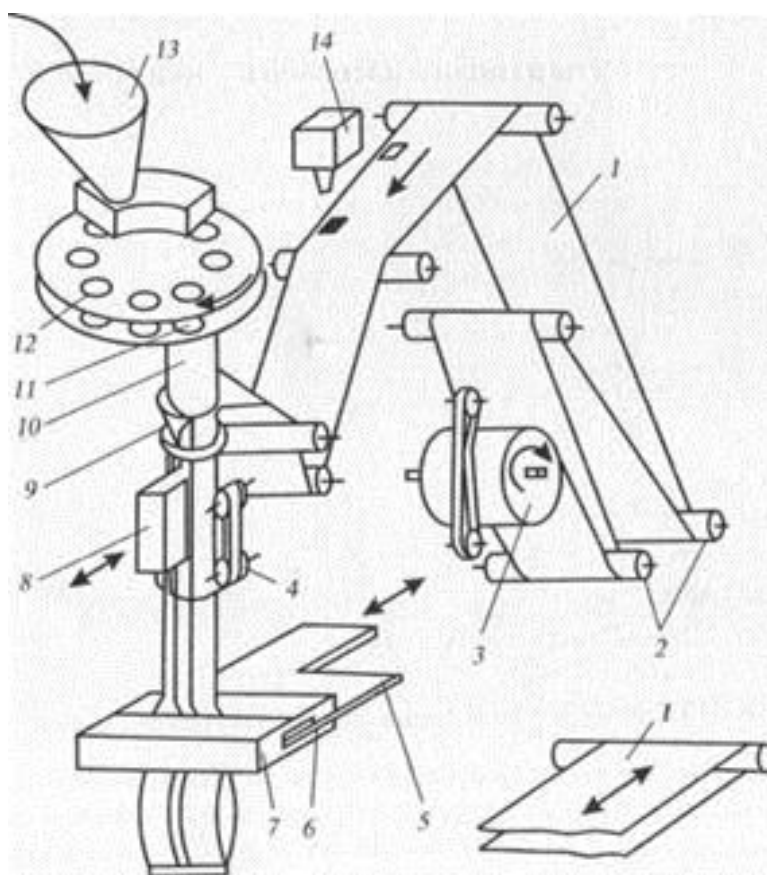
Технологічна схема автомата А5-КЛШ: 1 – полімерна стрічка; 2 – направляючі ролики; 3 – рулон стрічки; 4 – транспортер; 5 – верхній ніж; 6, 7 – губки поперечного зварювання; 8 – губка подовжнього зварювання; 9 – рукавоутворювач; 10 – труба; 11 – позиція відкриття денця; 12 – мірні склянки; 13 – приймальний бункер; 14 – фотоелемент
